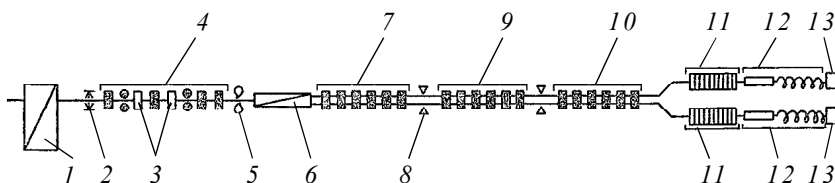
Схема расположения оборудования непрерывного проволочного стана:
